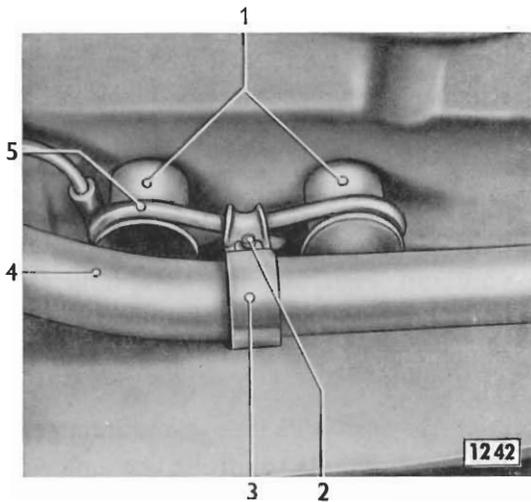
Befestigung des hinteren Auspuffrohres am Wagenboden
